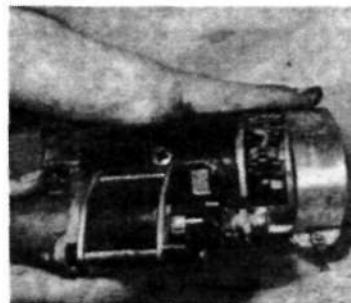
Вид якоря с конструкцией опережения сцепления
